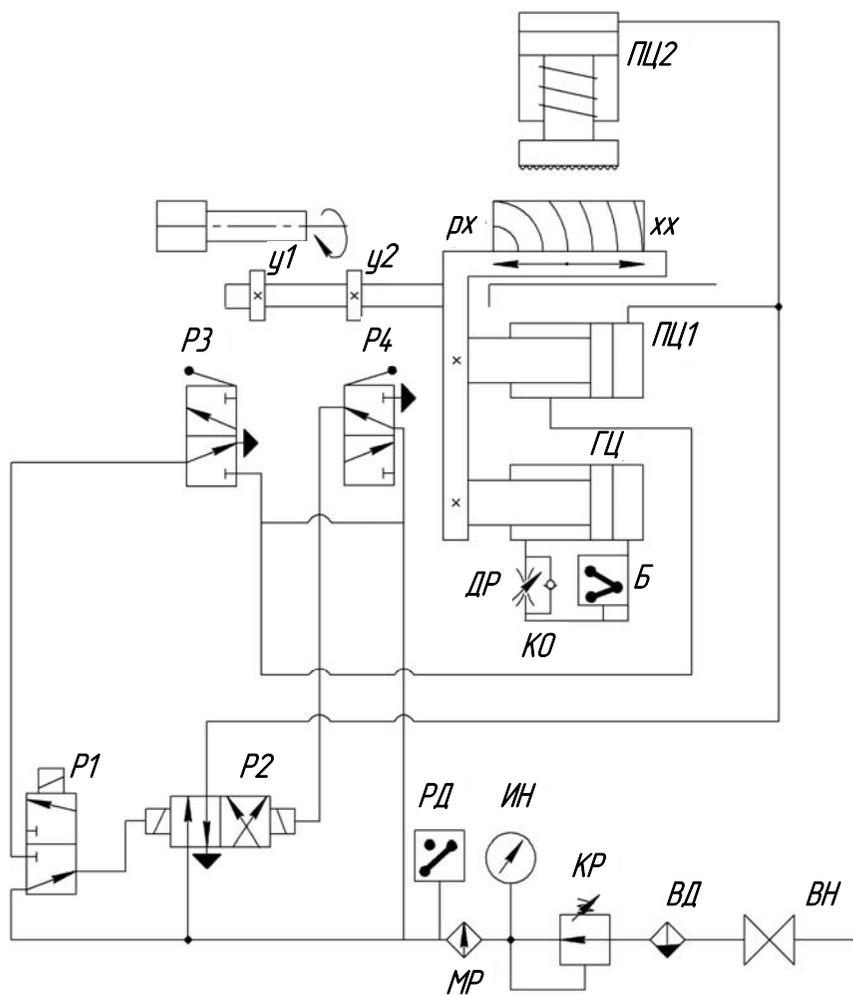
Пневматическая схема сверлильно-пазовального станка СВПГ-3
